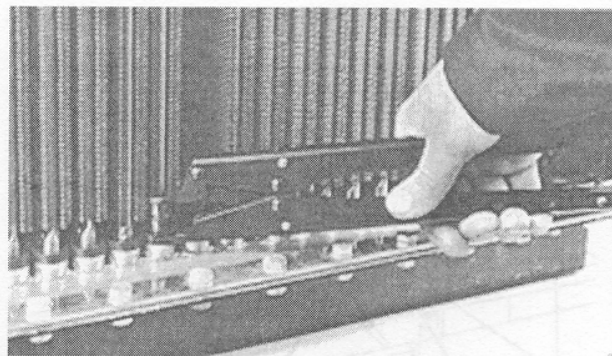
HERRAMIENTA DE MONTAJE (VJ6567)
